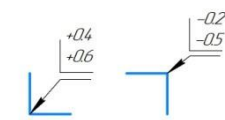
Модуль 1 Чертеж деталей Токарные работы на станках с ЧПУ
